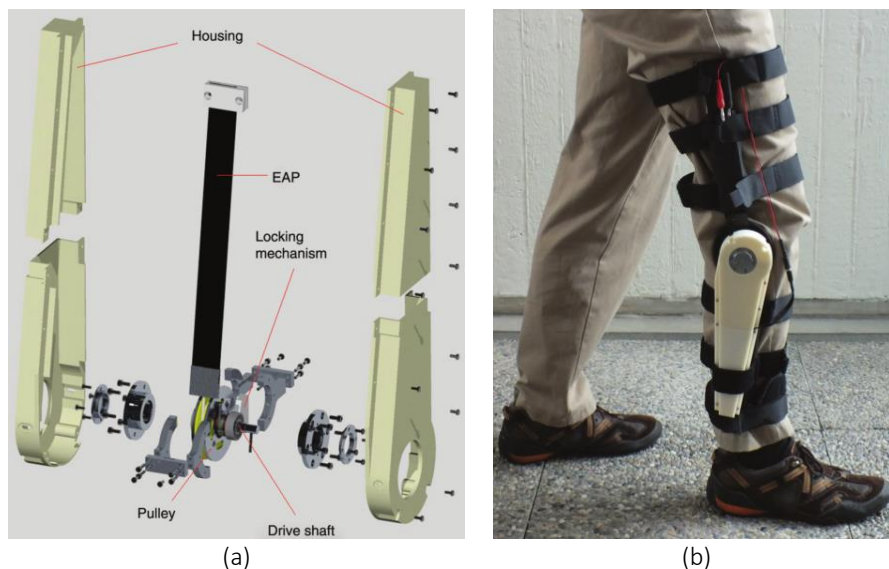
Prototype de DEG pour la conversion du mouvement du genou [153].
